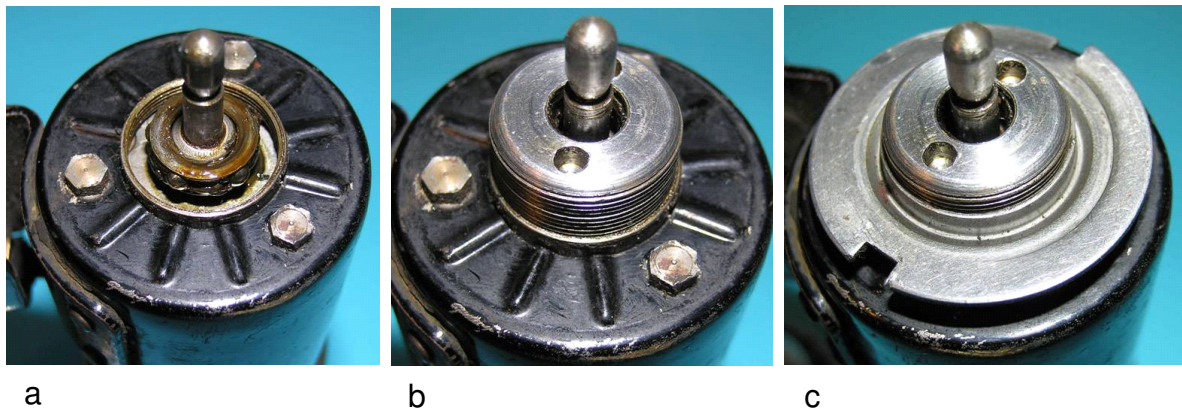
Unteres Lager: a) Innengewinde im Boden und Kugellager auf der Welle, b) im Boden eingeschraubte Lagerschale, c) Blechteller ausgeführt als Kontermutter und als Gewindegang zum Aufschrauben der Schalterkappe
